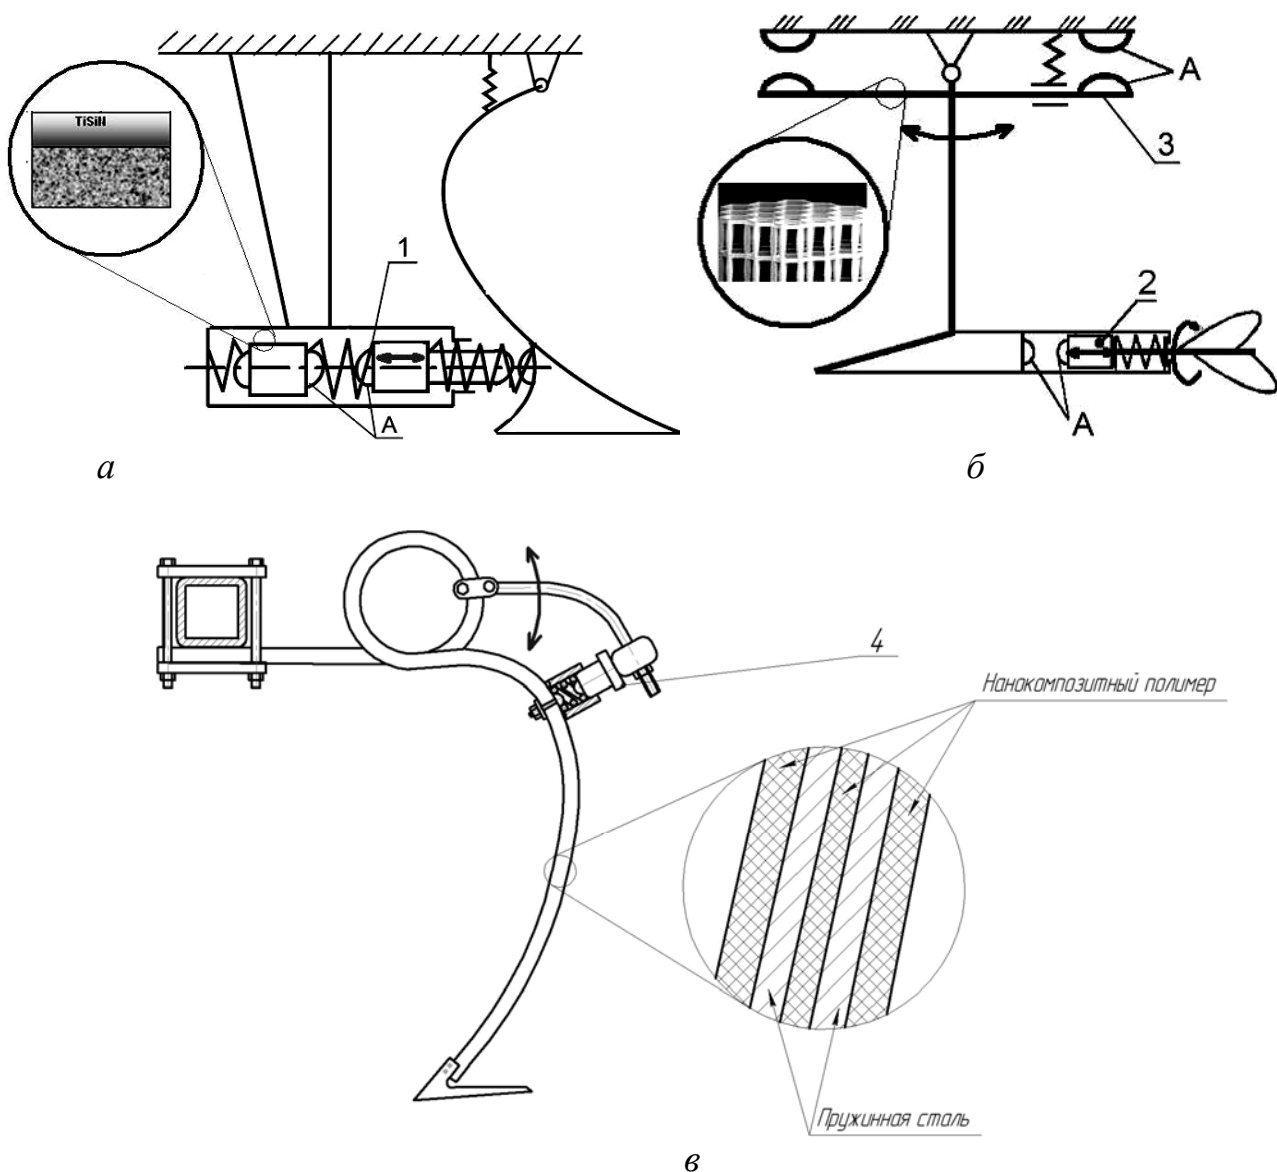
Схемы рабочих органов с виброударными механизмами
